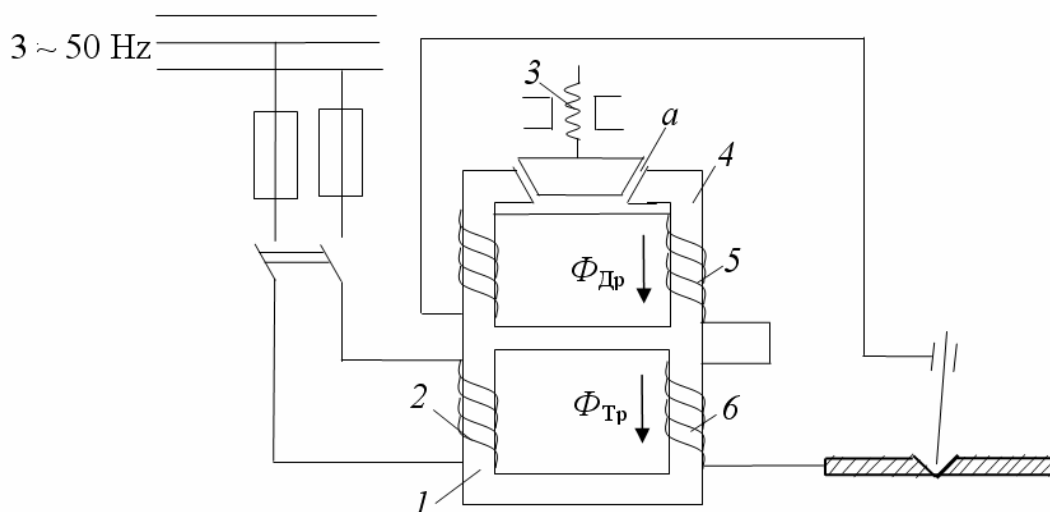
Схема сварочного трансформатора со встроенным дросселем:
